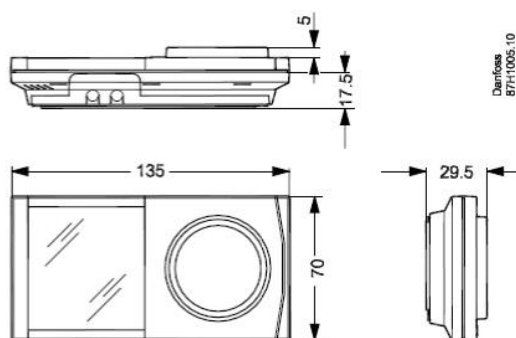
Габаритные и присоединительные размеры ECA 30/31.
